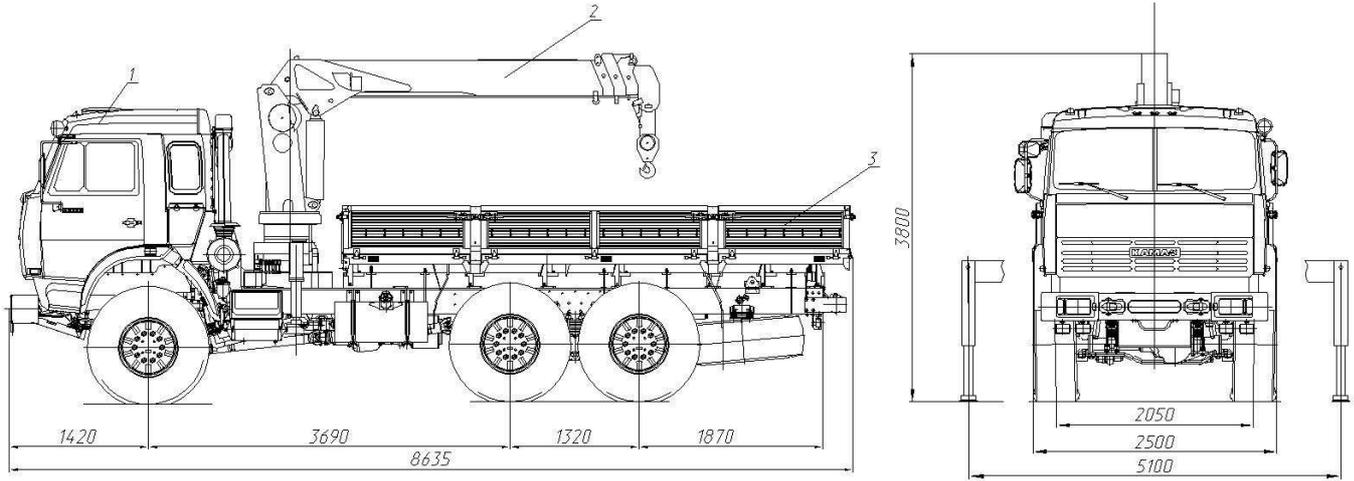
а - Общий вид 333805 на шасси КАМАЗ-43118-10
